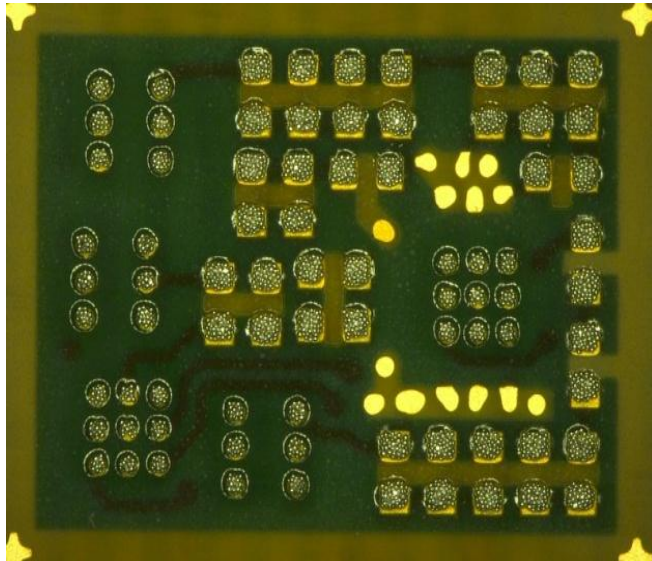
Impresión de soldadura de pasta a 1:1 No reducción abertura cuadrada
